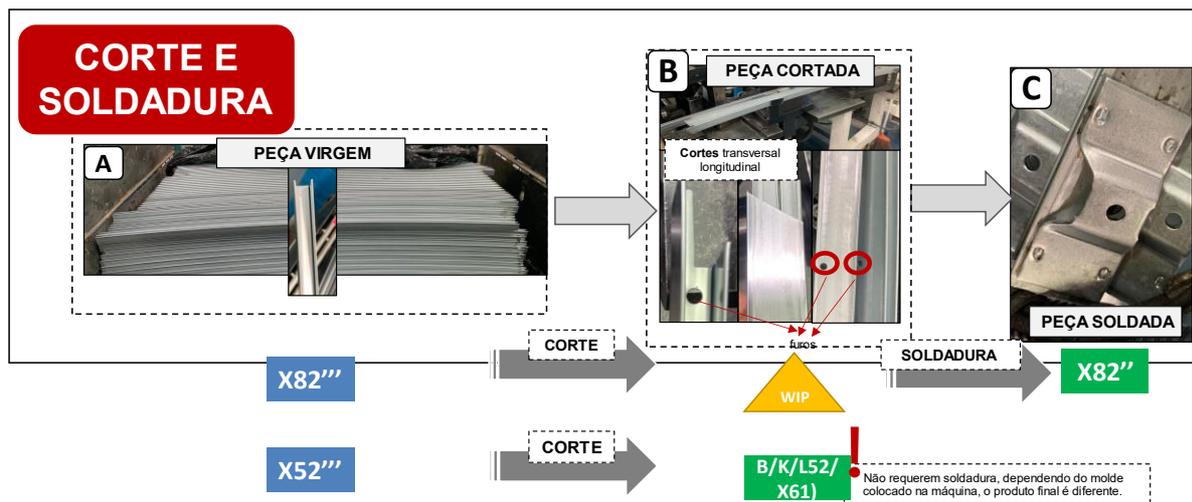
“Corte e Soldadura” na guilhotina do X82
